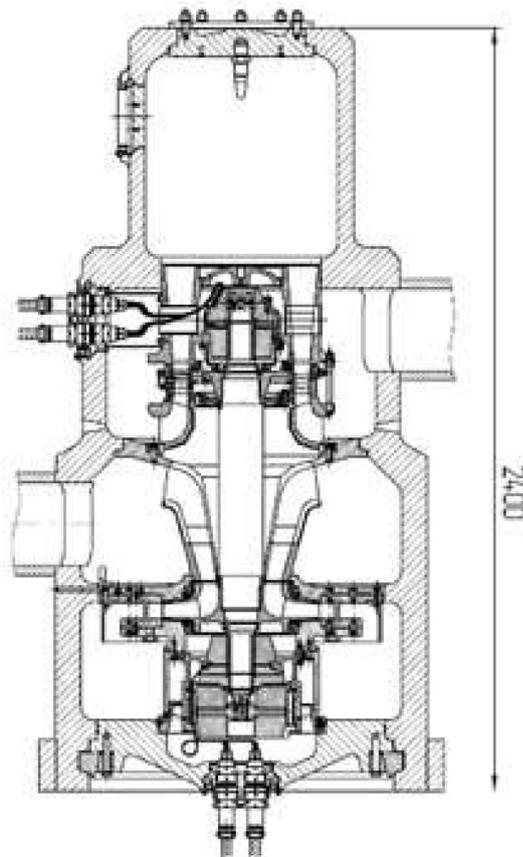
Турбодетандерный агрегат АДКГ-6-20/17-УХЛ4 с центробежным компрессором серии ТК
